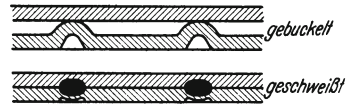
Buckelschweißung zweier Bleche.
